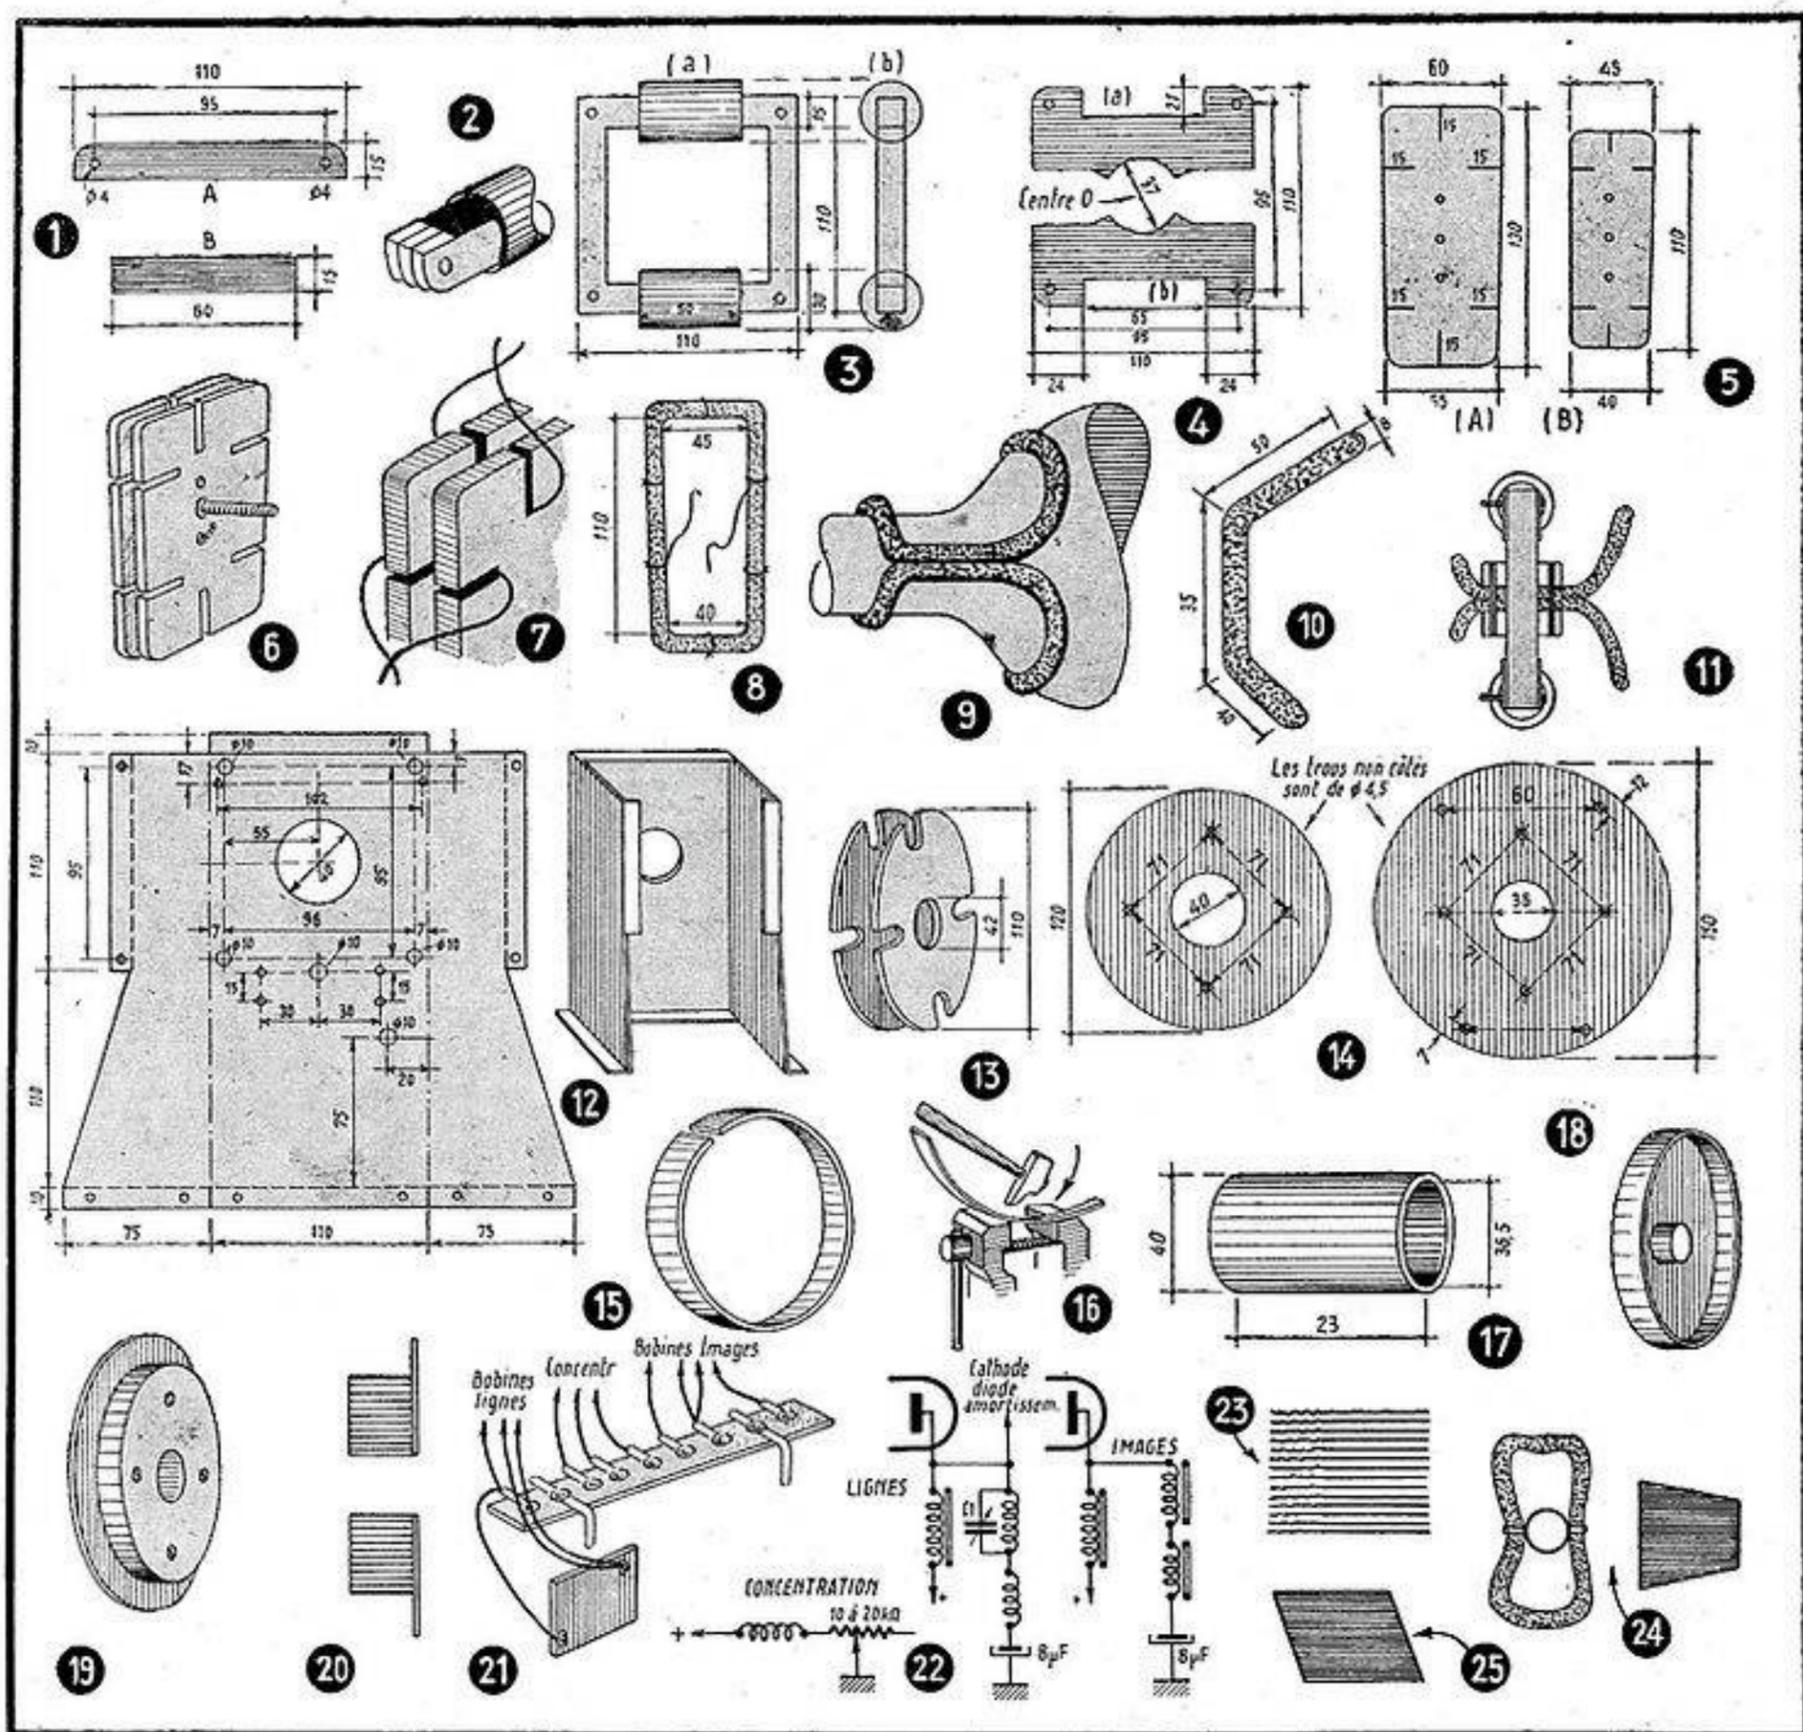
Dimensions des côtes des bobines images. — fig. 2. - Disposition des tôles dans le noyau. — fig. 3 - Montage de l'ensemble de déviation verticale. — fig. 4 - Découpage des joues. — fig. 5 - Forme et joues pour exécuter les bobines de lignes. — fig. 6 - Assemblage du moule à bobiner. — fig. 7 - Attache des fils. — fig. 8 - Bobine terminée. — fig. 9 - Bobines lignes montées sur le tube. — fig. 10 - Cambrure des bobines. — fig. 11 - Assemblage des bobines lignes et images. — fig. 12 - Bâti-support. — fig. 13 - Bobine de concentration. — fig. 14 - Flasques métalliques. — fig. 15 - Tôle annulaire. — fig. 16 - Cambrure de la tôle annulaire. — fig. 17 - Tube central. — fig. 18 - Assemblage du blindage. — fig. 19 - Coquille complète. — fig. 20 - Coupe du blindage. — fig. 21 - Montage des cosses. — fig. 22 - Schéma d'utilisation. — fig. 23 - Ondulation des débuts de lignes. — fig. 24 - Distorsion en trapèze. — fig. 25 - Distorsion en parallélogramme.
